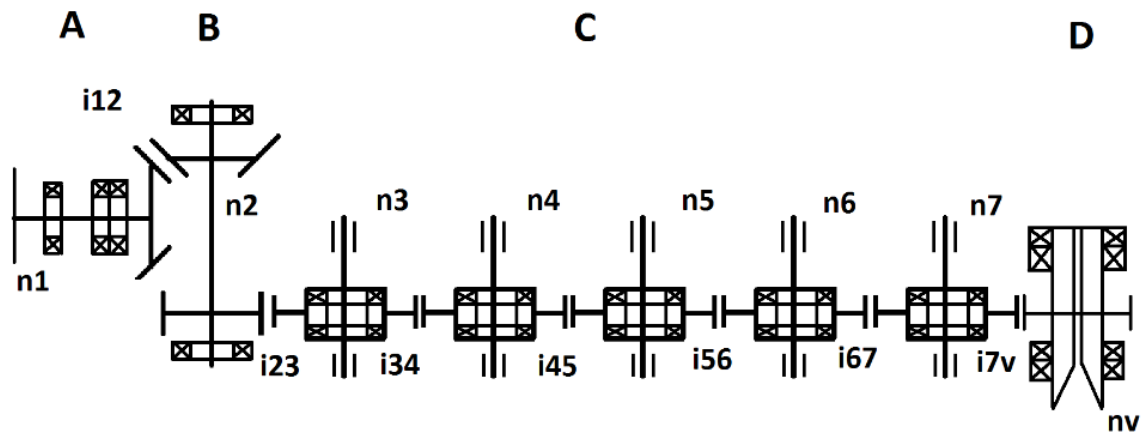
Kinematické schéma frézovací hlavy s horizontální hřídelí
